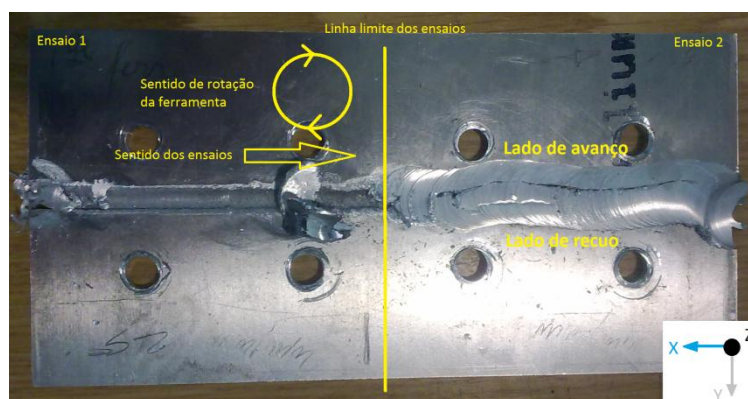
Aspetto do provete após ensaio com a ferramenta número 1
